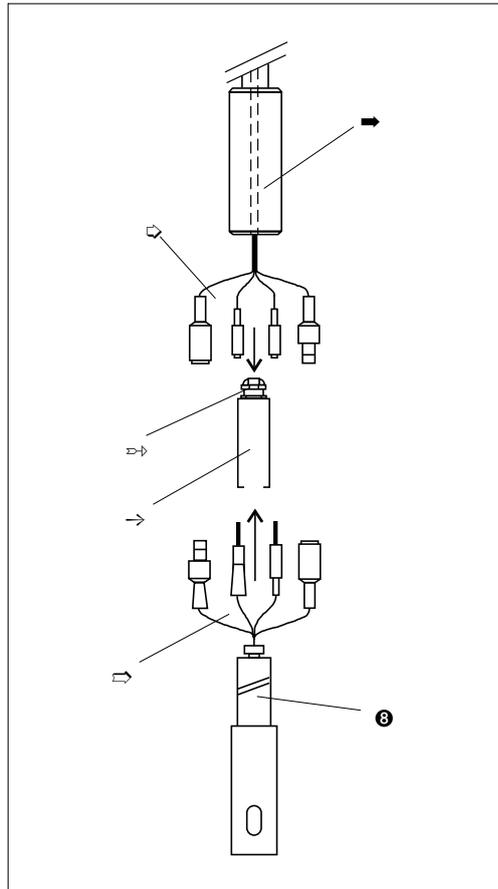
Kabelanschluß und Montage des Sensors bei Eintauchversionen
